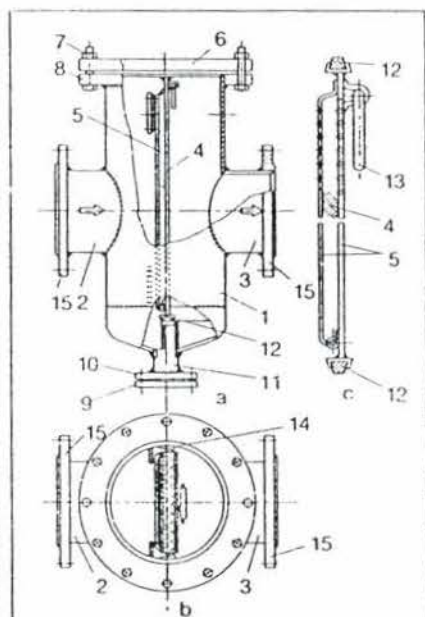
Filtru pentru gaze combustibile naturale:
